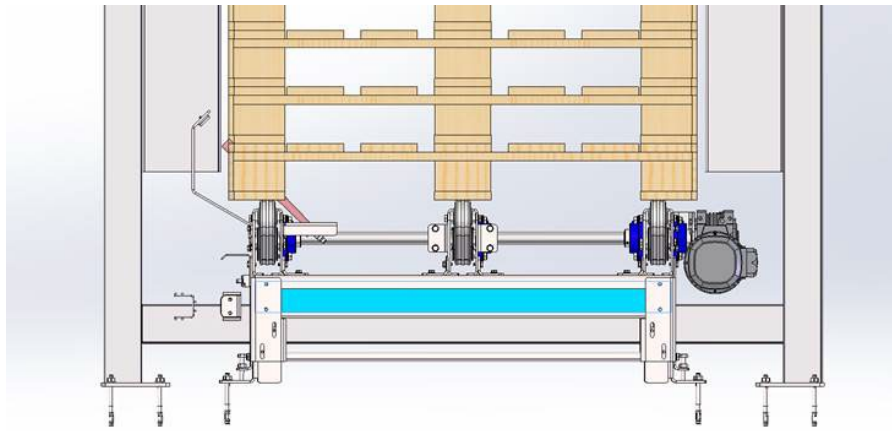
Vista frontal de pallets tipo Arlog en cadena de entrada de pallets.
